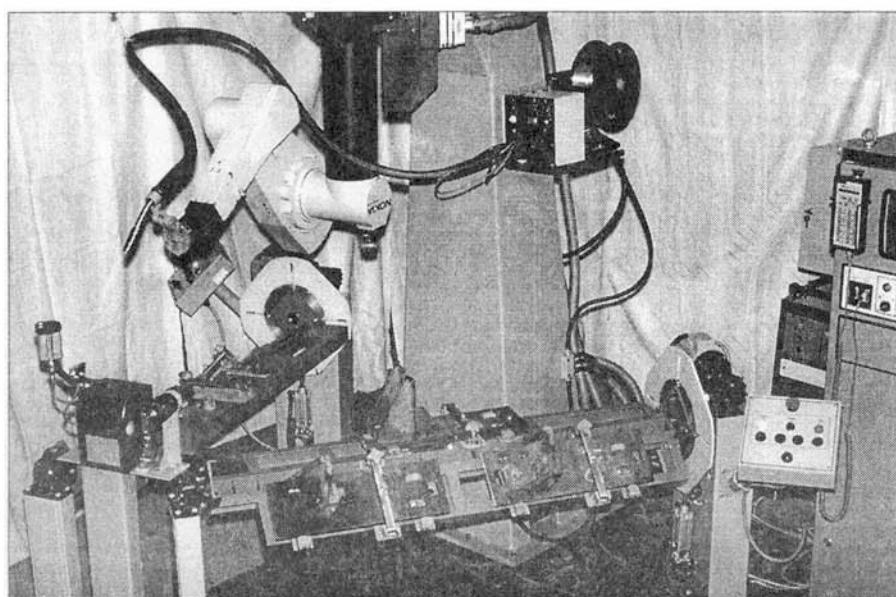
Робототехнический комплекс для дуговой сварки стойки с подкладкой
